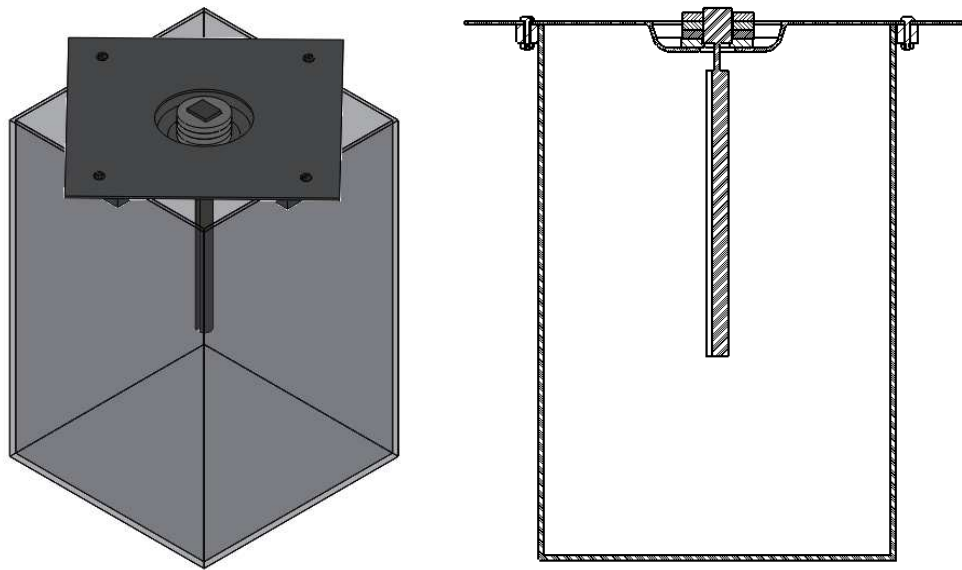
Modelo del conjunto en 3D (izquierda) y vista de corte del conjunto (derecha).
